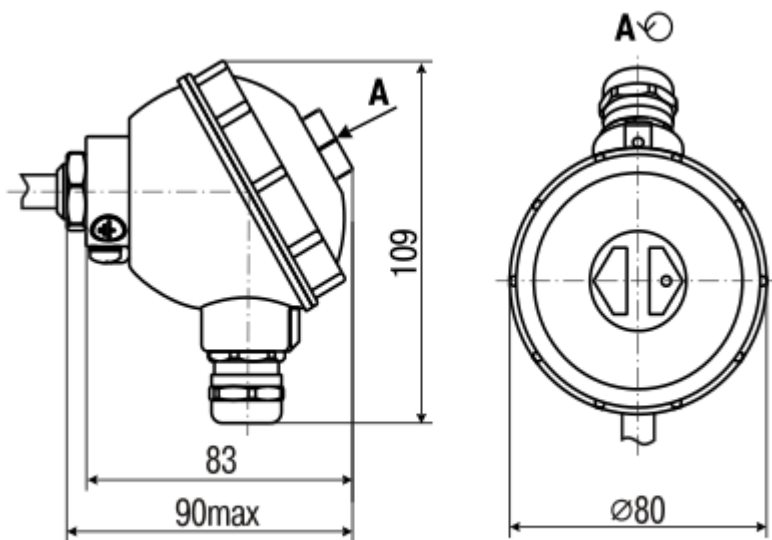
Габаритный чертеж коммутационной головки
